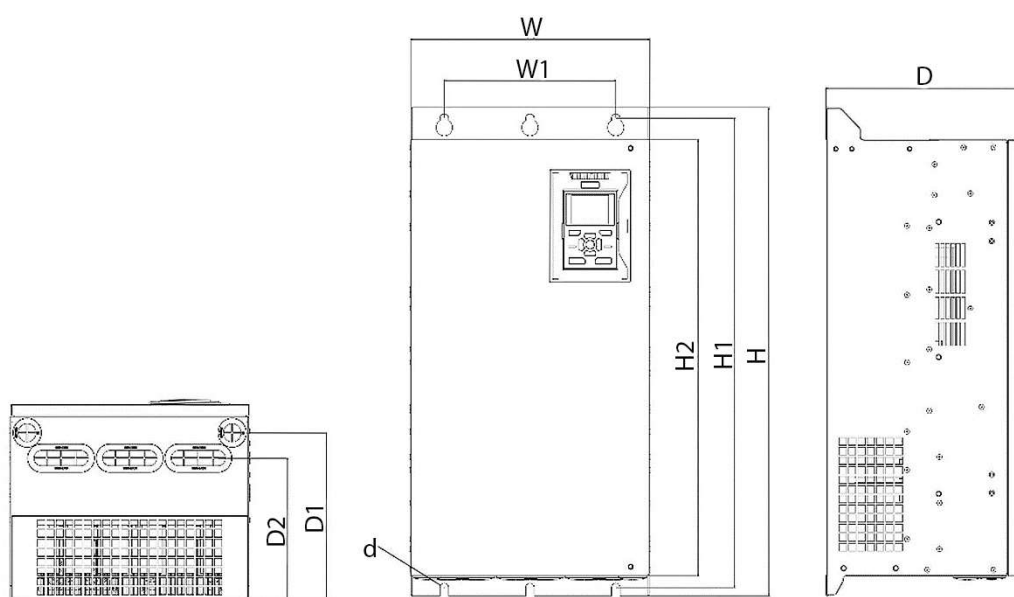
Внешний вид преобразователей E5-9600-040H...500H, E5-9600-025K...500K
